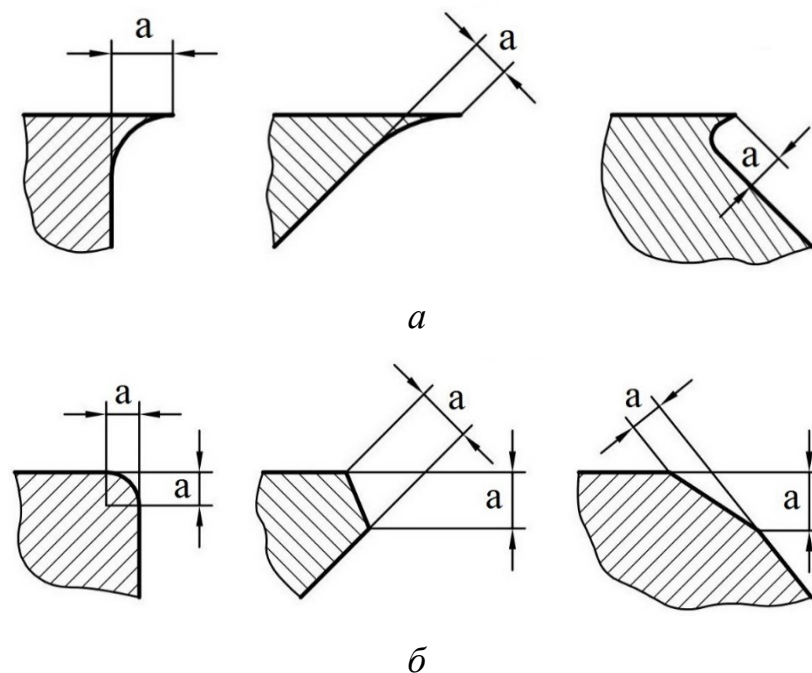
Типові форми задирок, що утворюються при торцевому фрезеруванні [37]
